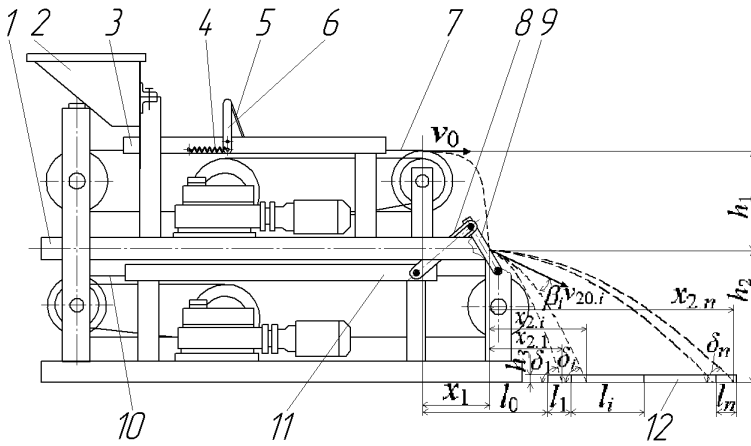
Схема удосконаленого пристрою для сортування ТПВ: 1 – корпус; 2 – завантажувальний бункер; 3, 11 – борти; 4 – пружина розтягу; 5 – похила металева планка; 6 – П-подібна рама; 7 – верхній транспортер; 8 – стійки; 9 – похила металева плита; 10 – нижній транспортер; 12 – багатосекційний контейнер
